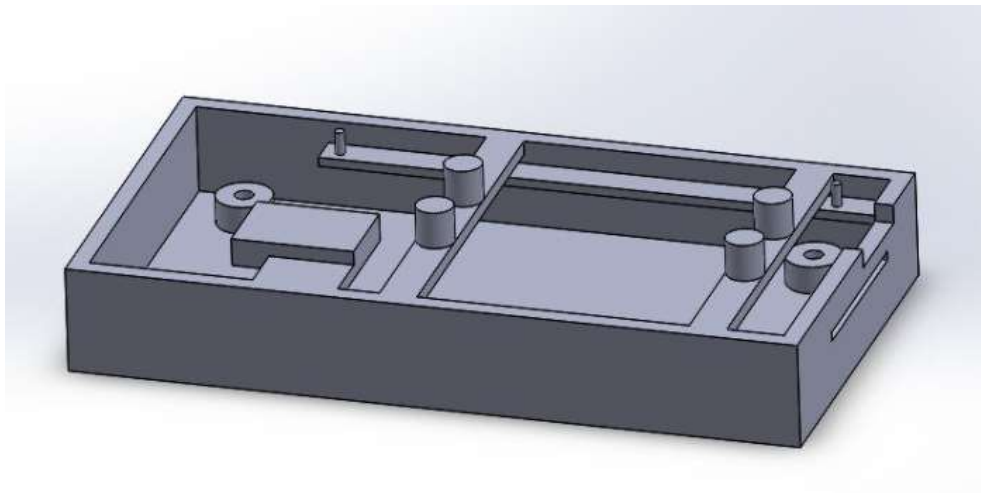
3D конструкція нижньої частини корпусу.
